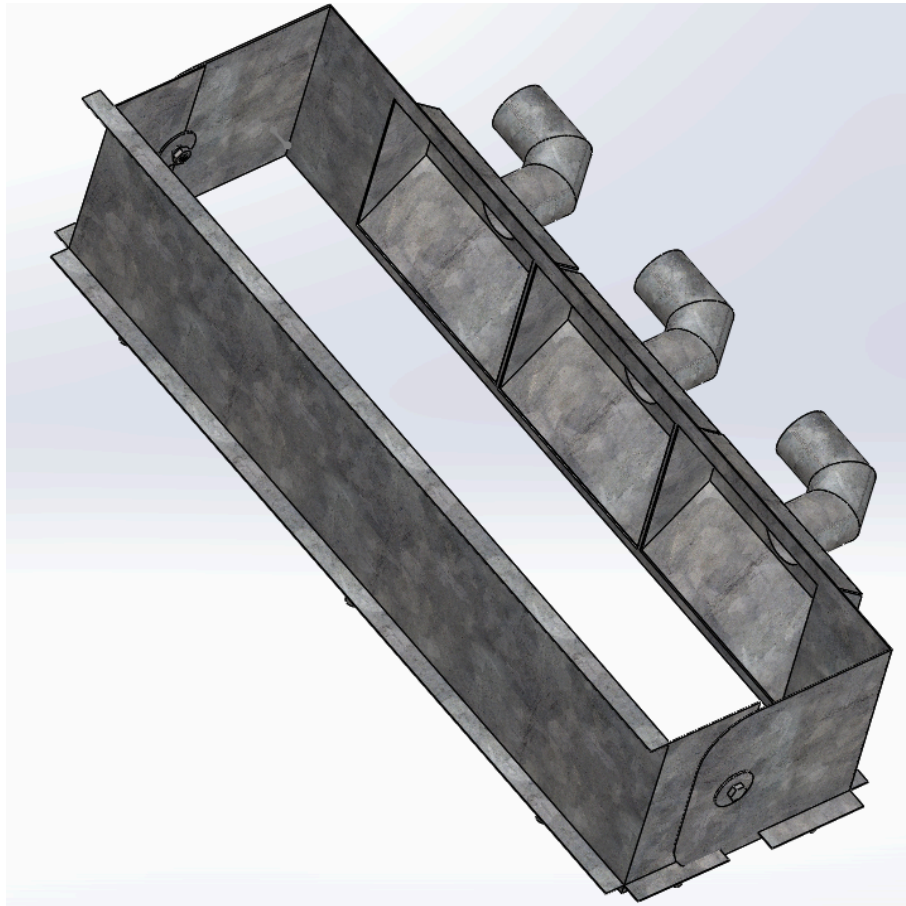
Diseño 3D del Módulo de Contención para Soldadores (MCS)
